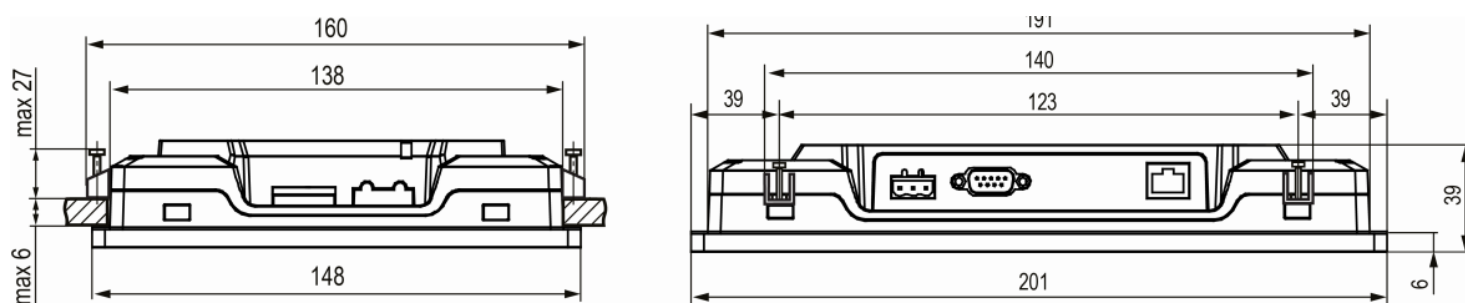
DIMENSIUNI de DETALIU SPC210-07
